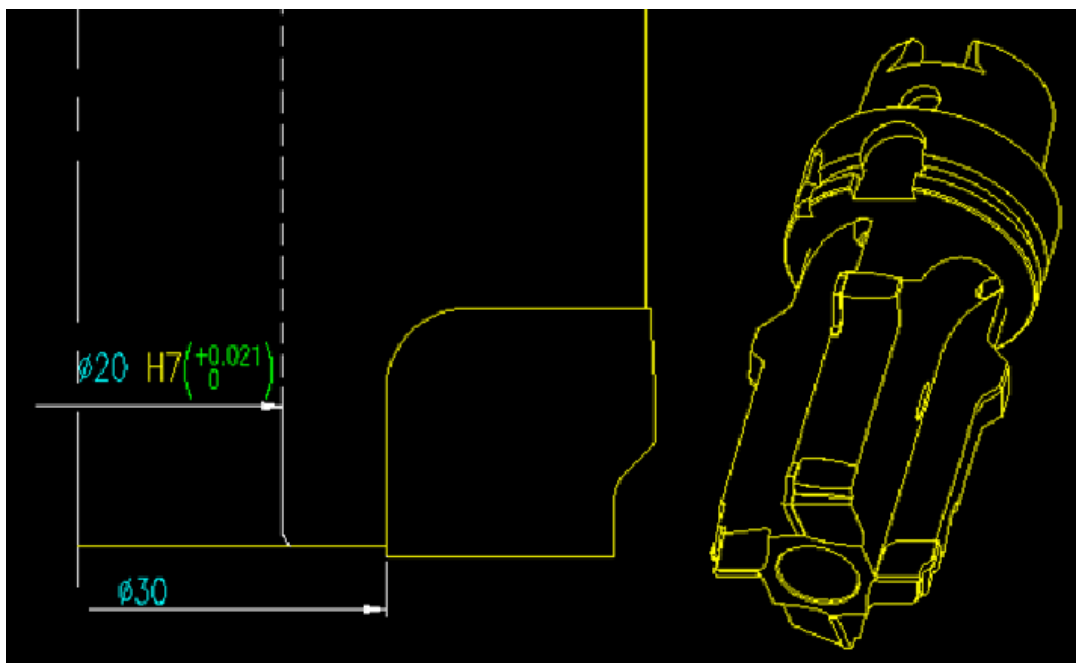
Desenho técnico de uma ferramenta YR com PCD
